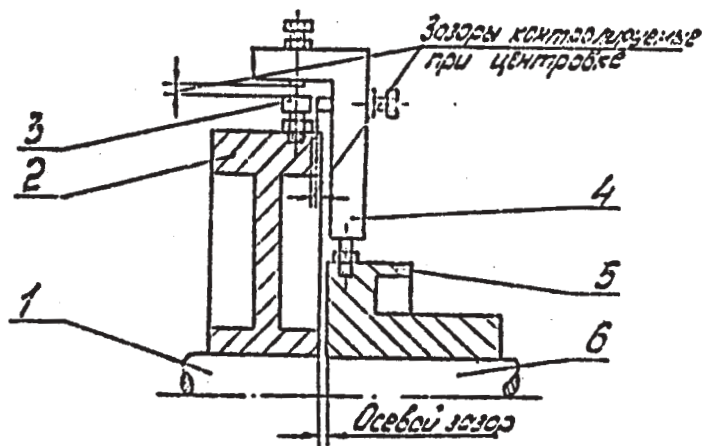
Схема установки приспособления при проверке центровки вала электродвигателя и компрессора
